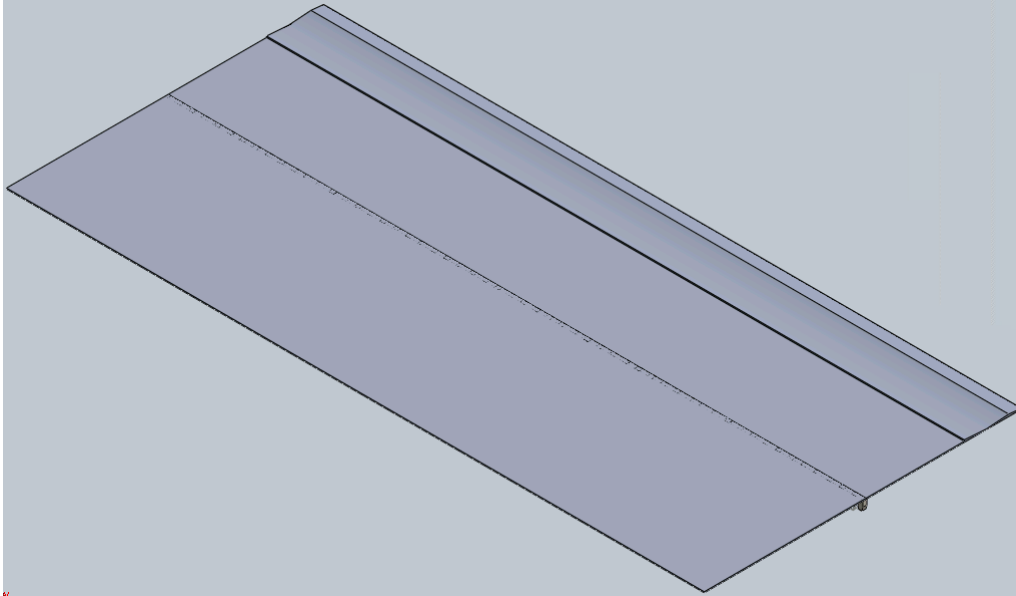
Plancha donde se posan los vehículos para su posterior transporte.
